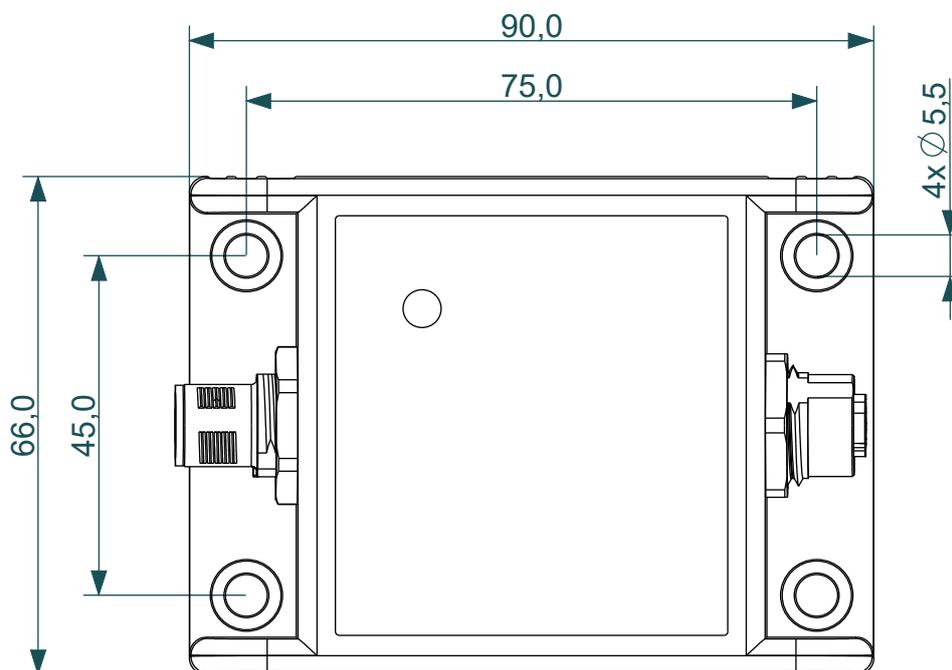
Befestigungsbohrungen (Maße in mm)
